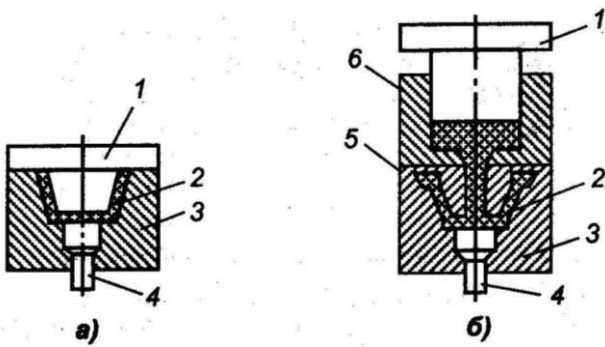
Схема прямого (а) та литтєвого (б) пресування заготовок з пластмас: 1 – пуансон; 2 – заготовка; 3 – матриці; 4 – виштовхувач; 5 – додатковий пуансон; 6 – підігрівна камера
